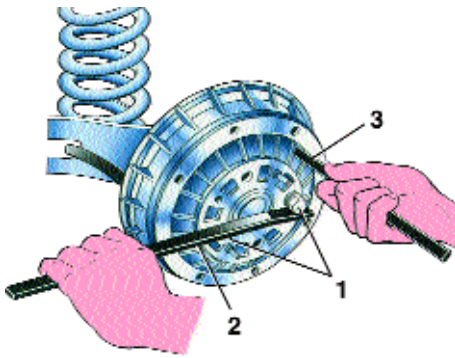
Сдвигание задней тормозной колодки на заднем тормозе при помощи трубчатой оправки при значительном износе барабана с образованием у него буртика: 1 – болты крепления колеса; 2 – рычаг (монтажная лопатка); 3 – трубчатая оправка с внутренним диаметром 12 мм
